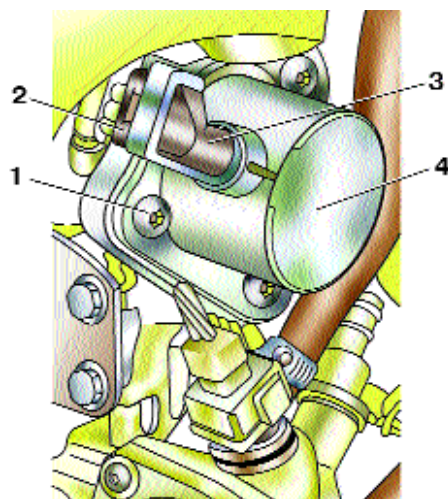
Крепление датчика порядкового номера цилиндра на двигателе: 1 – винт крепления; 2 – штекерный разъем; 3 – чувствительный элемент датчика; 4 – датчик
